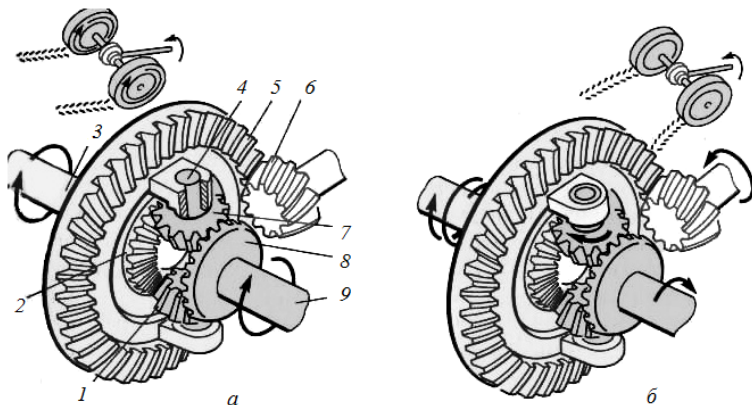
Конический симметричный дифференциал: а – устройство; б – схема работы; 1, 7 – шестерни-сателлиты; 2, 8 – полуосевые зубчатые колеса; 3, 9 – полуоси; 4 – крестовина; 5 – ведомое колесо главной передачи; 6 – ведущая шестерня главной передачи
